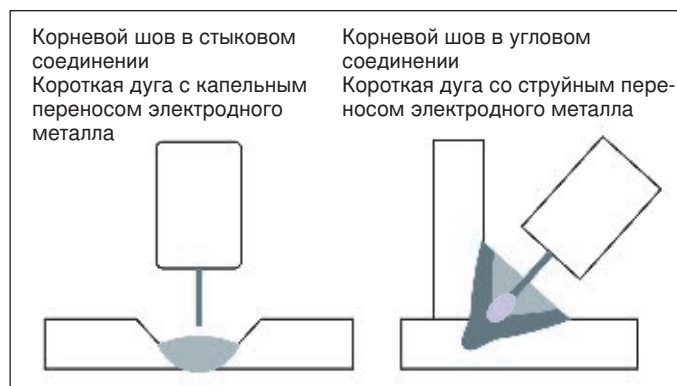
Режимы Steel Root — для сварки корневого шва и Steel Dynamic — для сварки концентрированной динамичной дугой
